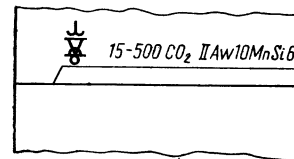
Схема, дополнительное изображение, размерные данные, метод сварки, класс исполнения, положение шва при сварке и присадочный материал
